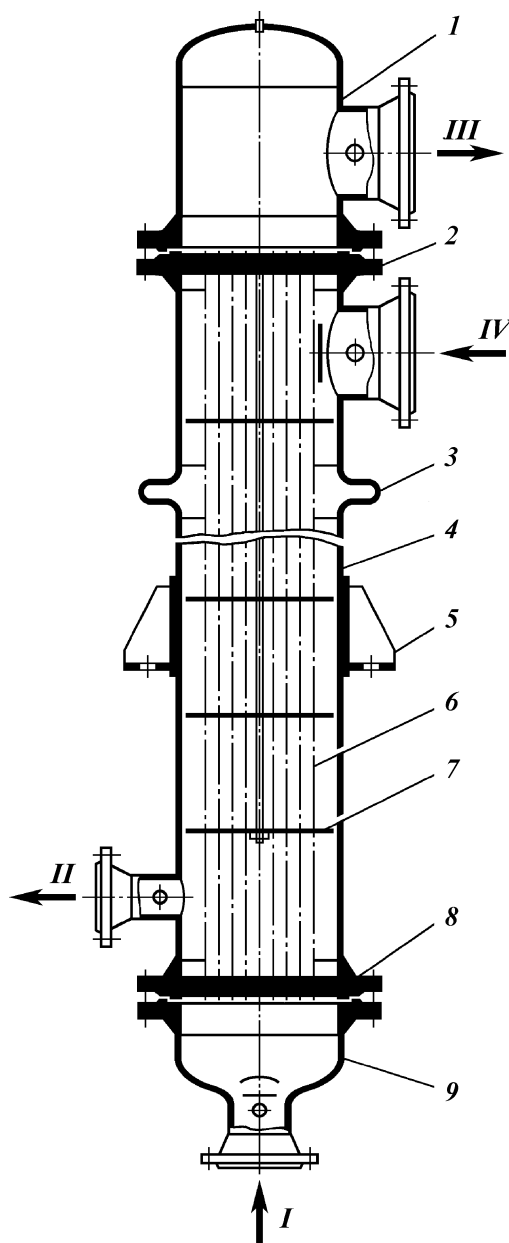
Вертикальный кожухотрубчатый испаритель с неподвижными трубными решетками и температурным компенсатором на корпусе:
